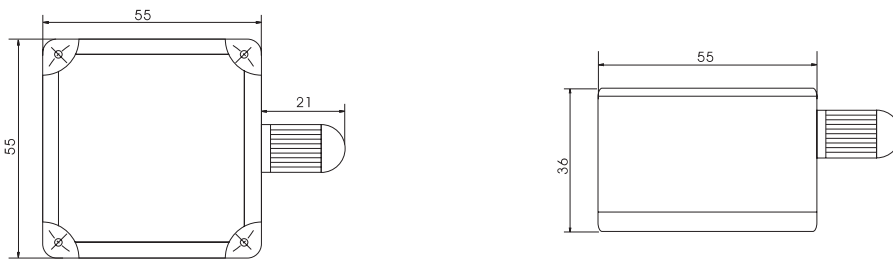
Klemmkasten KLM | Fig. 3 : Terminal box KLM
